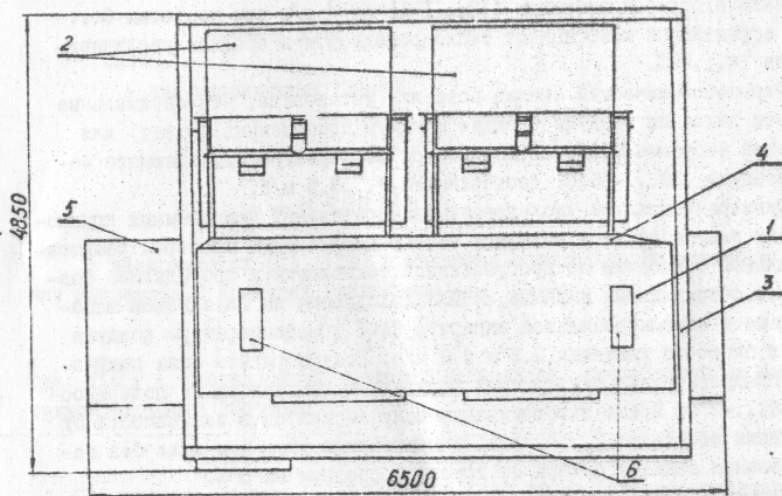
Скороморозильный виброконвейерный аппарат (вид сверху)
